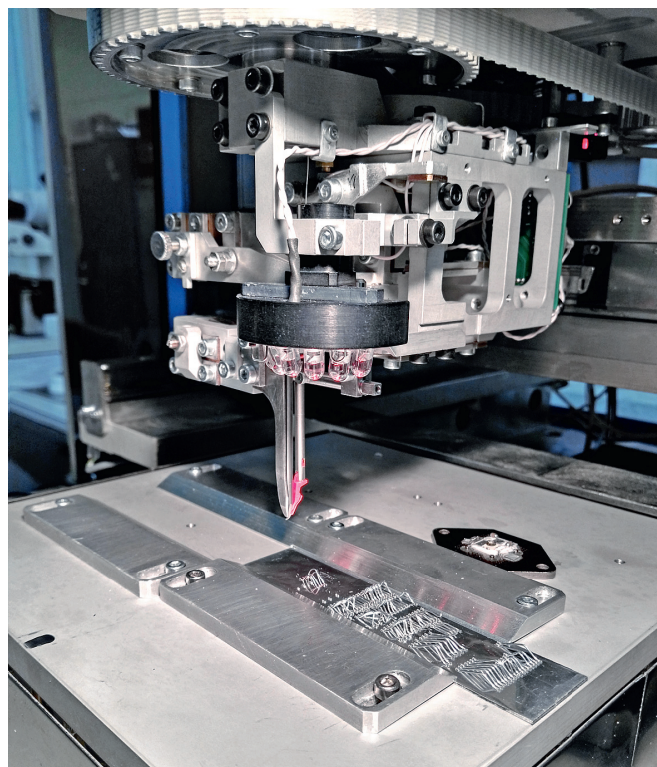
Сварочная головка установки ЭМ-4341
